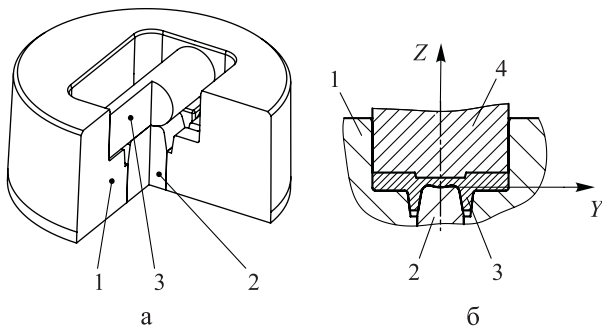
Установка заготовки в полости штампа (а) и схема процесса закрытой объемной штамповки фланца (б): 1 – матрица; 2 – контрпуансон; 3 – заготовка; 4 – пуансон
